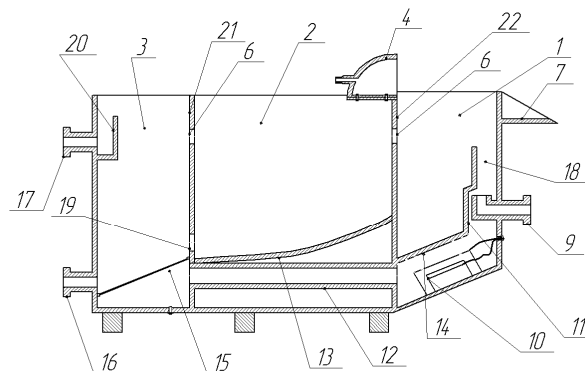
Устройство для очистки сточных вод: 1 – камера коагулирования; 2 – камера отстаивания; 3 – выпускная камера; 4 – щелевой коллектор; 5 – камера смешения воздуха и ингибитора; 6 – окна; 7 – пеноотводящий лоток; 8 – шламоприемник; 9 – патрубок для подачи исходной воды; 10 – растворимые электроды (анод и катод); 11 – перфорированная перегородка; 12 – трубопровод; 13 – наклонная поверхность; 14 – электродная камера; 15 – фильтративная сетка; 16 – патрубок для отвода осадка; 17 – патрубок для отвода очищенной воды; 18 – эжекционное устройство; 19 – окно для отвода осадка; 20 – карман для отвода очищенной воды; 21 – перегородка, разделяющая камеру отстаивания от выпускной камеры; 22 – перегородка, разделяющая камеру коагулирования от камеры отстаивания
